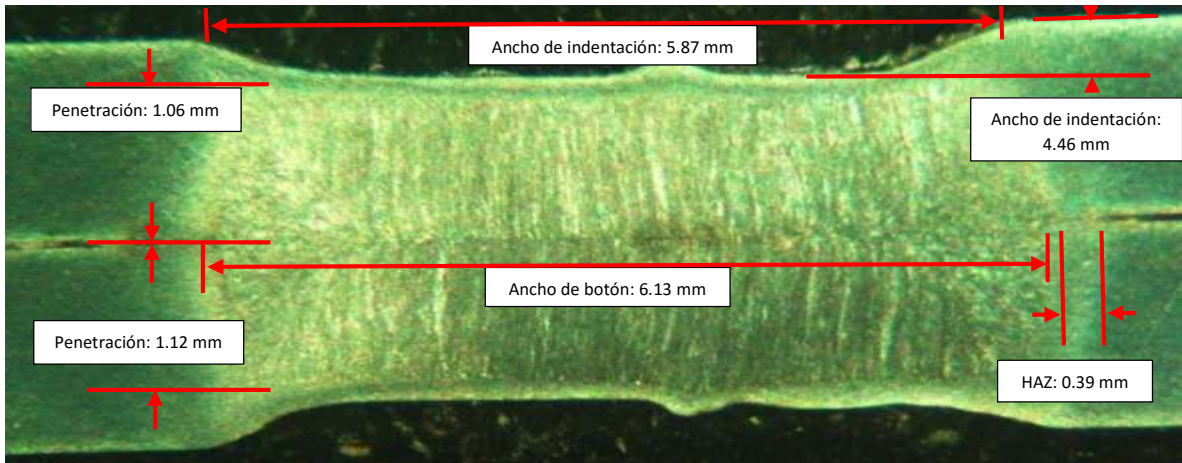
Mediciones realizadas en el botón de soldadura número 2.
